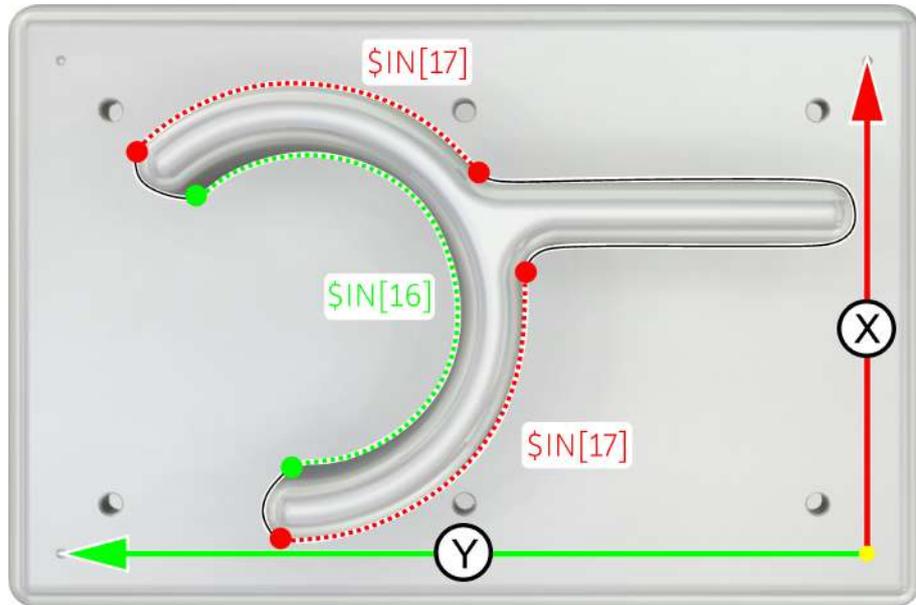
Componente de soldadura, conmutación de trayectoria
